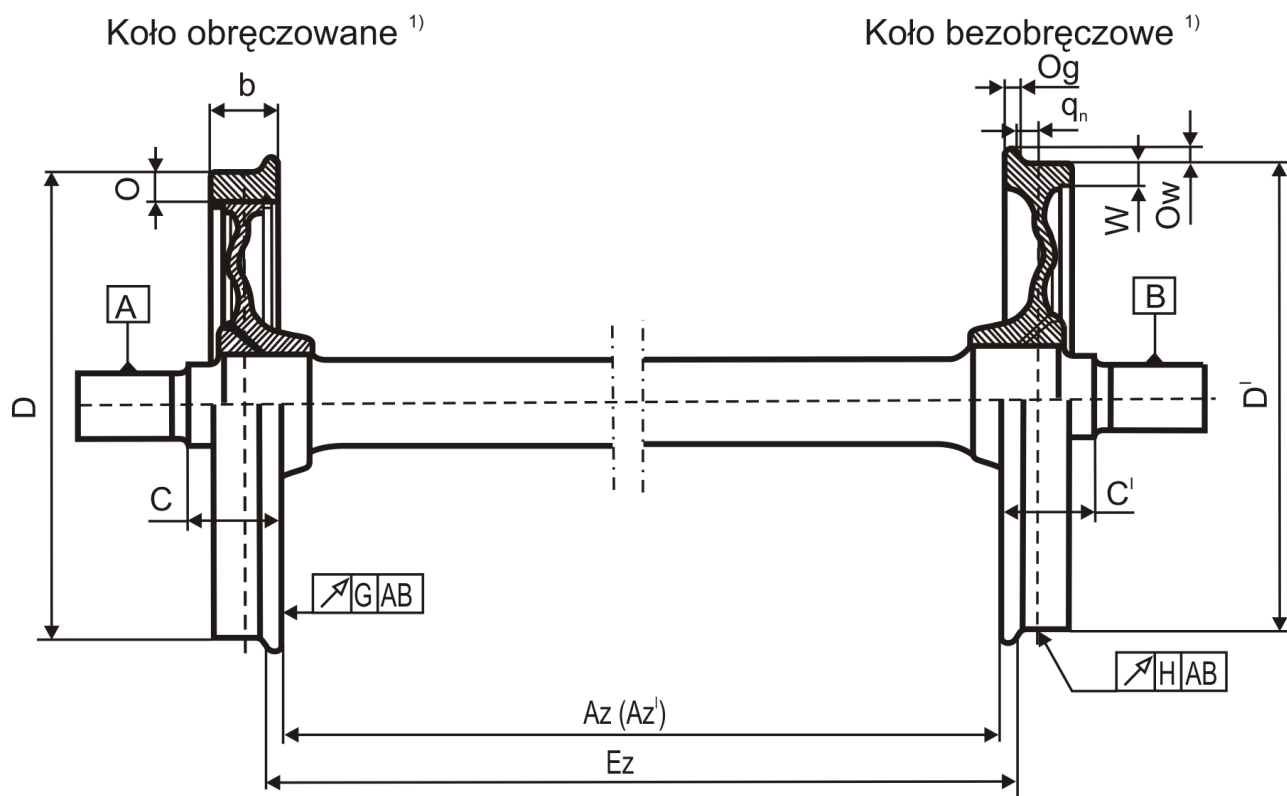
Oznaczenia i nazwy elementów zarysu zewnętrznego obręczy i kół bezobrzęczowych zestawów kołowych.
